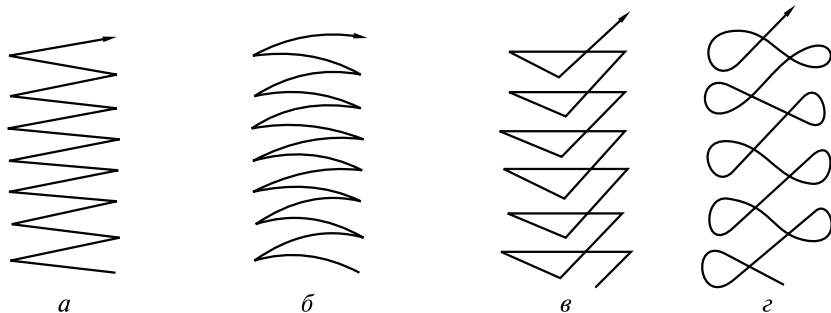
Колебательные движения электрода при ручной сварке:
